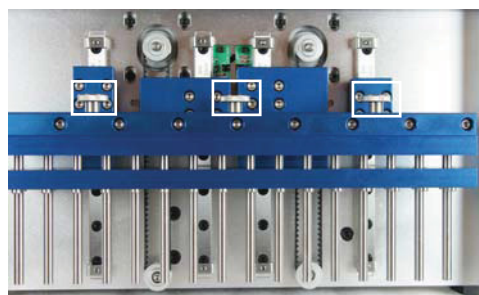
Ensemble de tiges magnétiques SEV avec les vis à serrage à main.
